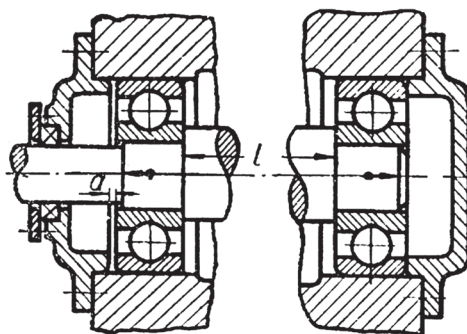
Подшипниковая сборочная единица, извлекаемая из корпуса
